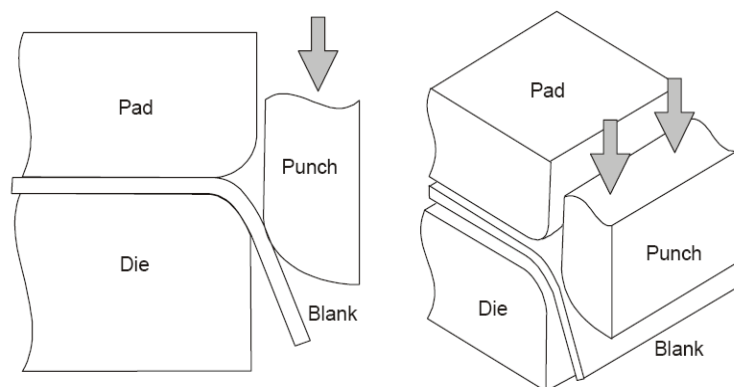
Quinagem de Flange com punção de arraste (wiping die bending).
